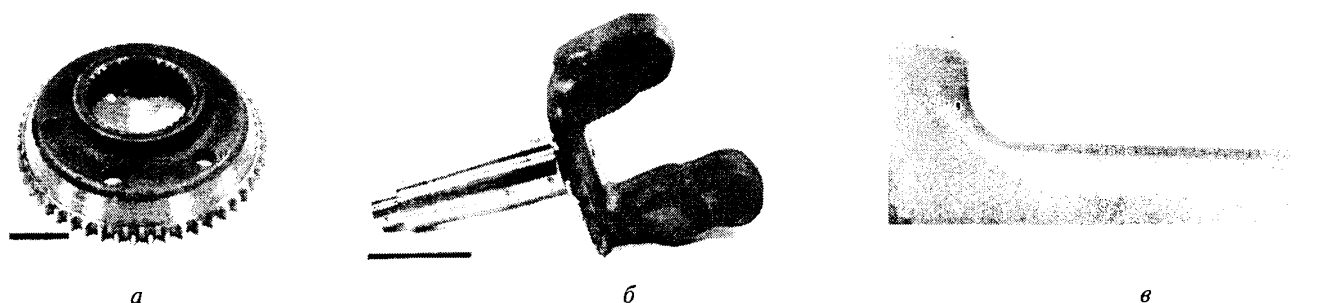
Ступица колесной передачи (а), поворотный кулак (б) автомобиля МАЗ, упрочняемые прерывистой закалкой и расположение зоны закалки на цилиндрической части и галтели кулака (в). Сталь 40Х
